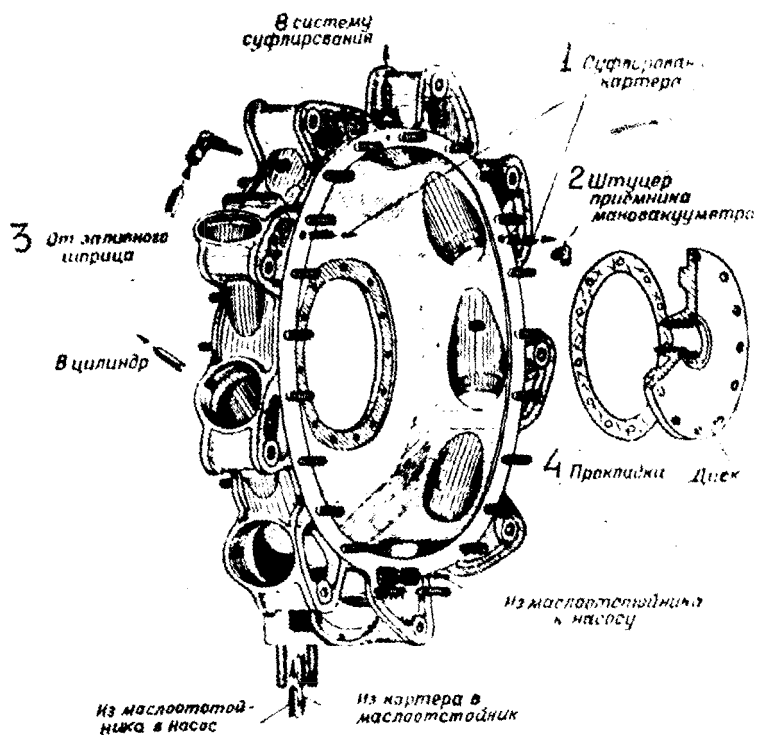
Передний корпус нагнетателя: 1—суфлирующие отверстия; 2—штуцер приемника мановакуумметра; 3—штуцер для заливки бензина; 4—прокладка корпуса нагнетателя
